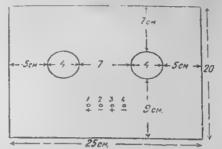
Разметка свинцового листа для изготовления чашечек.
